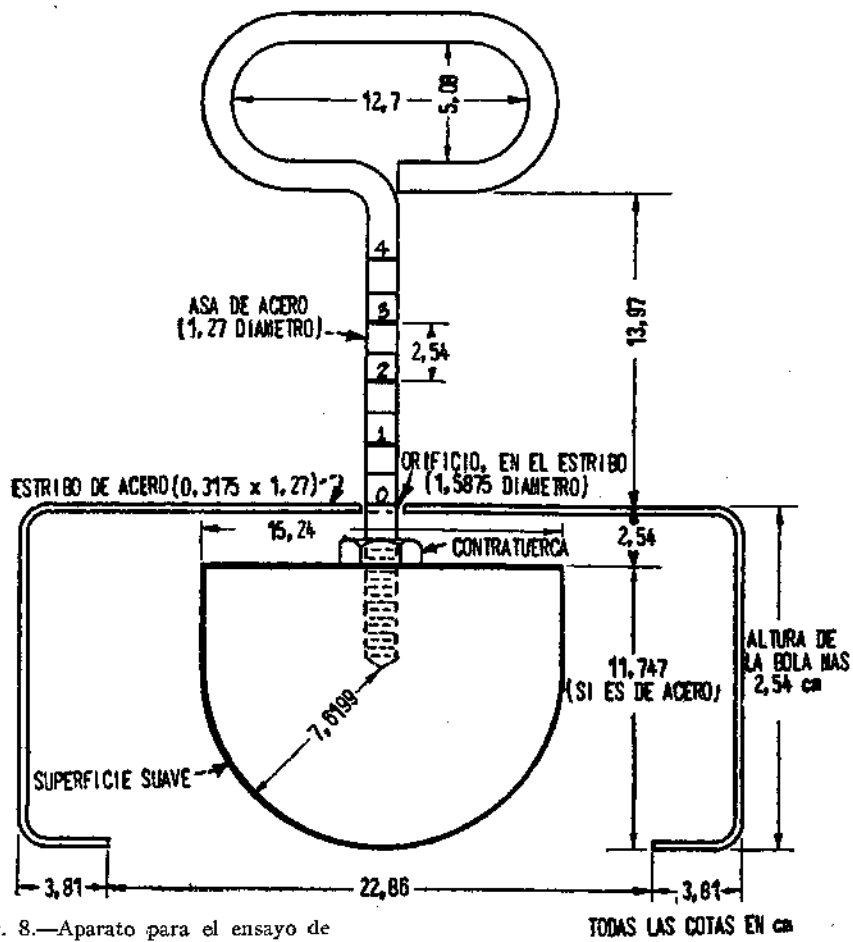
Aparato para el ensayo de penetración. Esquema acotado.
